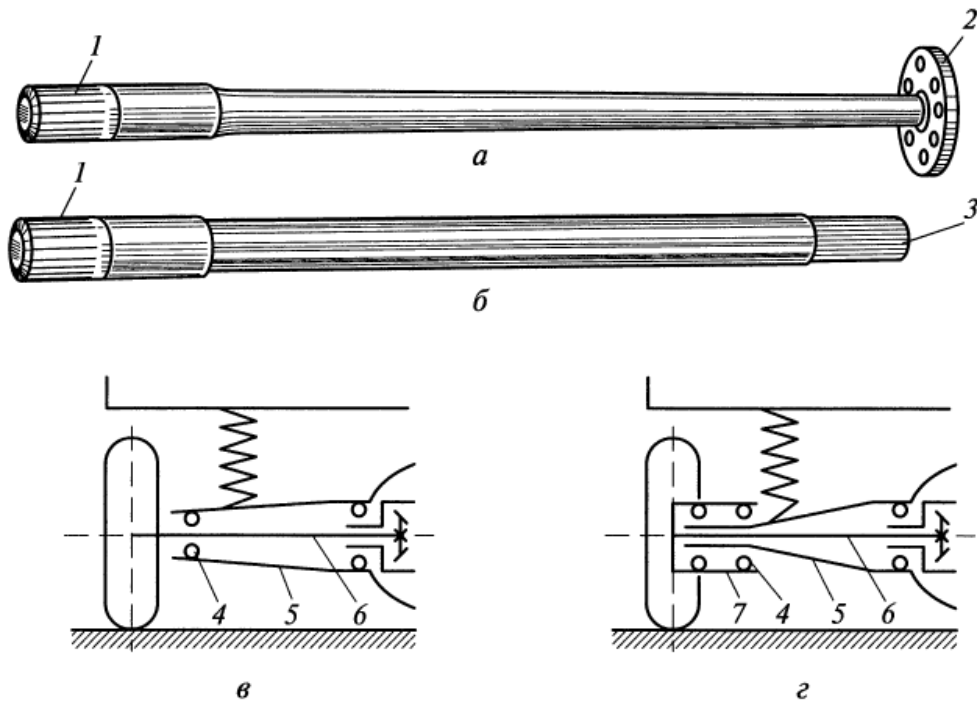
Піввісі: а - фланцева; б - безфланцева; в - напіврозвантажена; г - розвантажена; 1, 3 - шліцьові кінці; 2 - фланець; 4 - підшипник; 5 - балка; 6 - піввісь; 7 – маточина.
